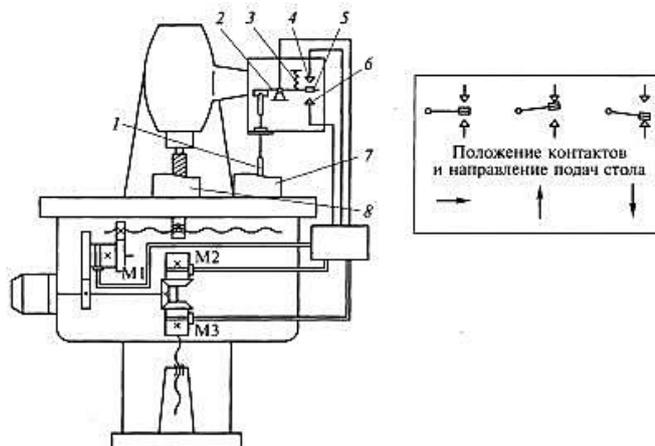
Схема электрокопировального станка с прерывистой следящей системой: 1, 3 — щуп; 2 — рычаг; 4, 5, 6 — контакты; 7 — копир, 8 - обрабатываемая деталь.
